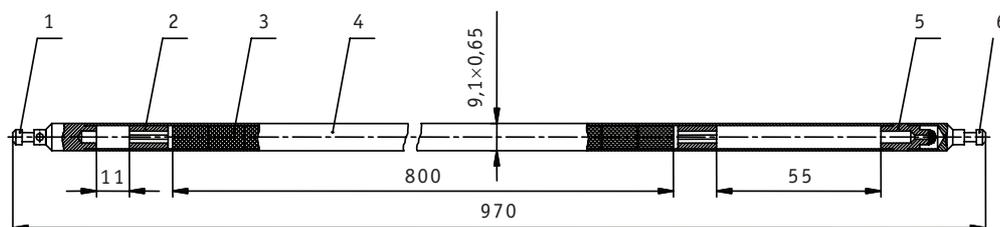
Твэл реактора ИВГ1.2М: 1 – нижняя заглушка; 2 – разрезная втулка; 3 – топливная таблетка; 4 – защитная оболочка; 5 втулка; 6 – наконечник
